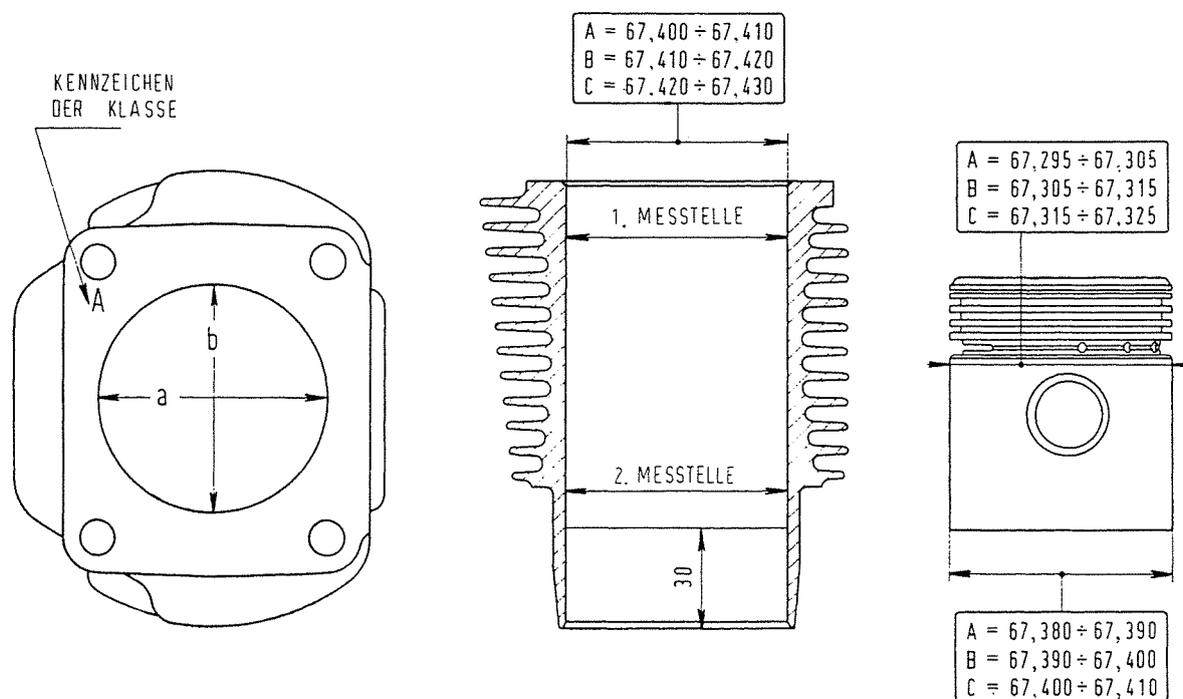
Hauptabmessungen der Zylinder und Kolben.
